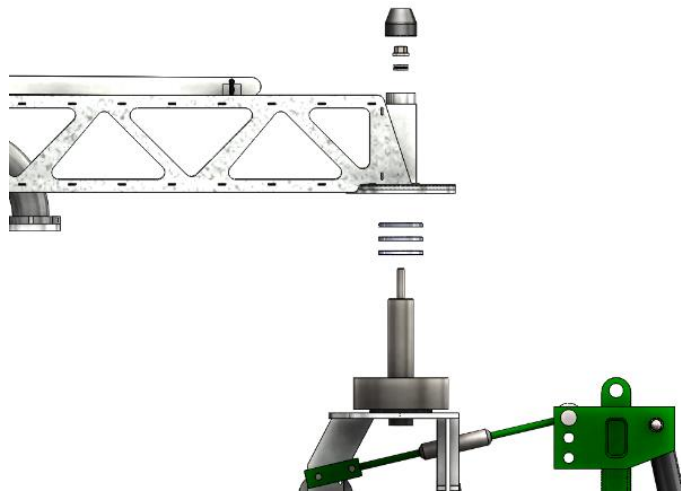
CAD - Explosionsansicht Vorspannsystem
